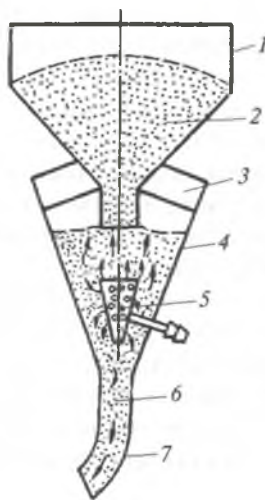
Схема бункера для газофлюсовой защиты сварочной ванны:
